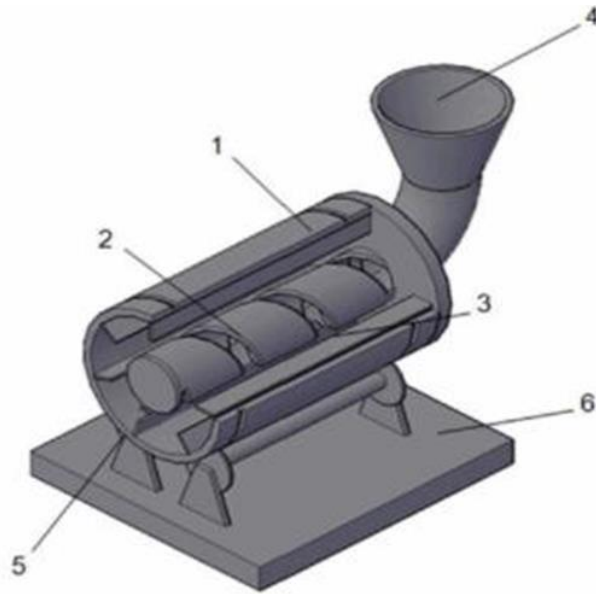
Барабанный смеситель с цилиндрической вставкой
